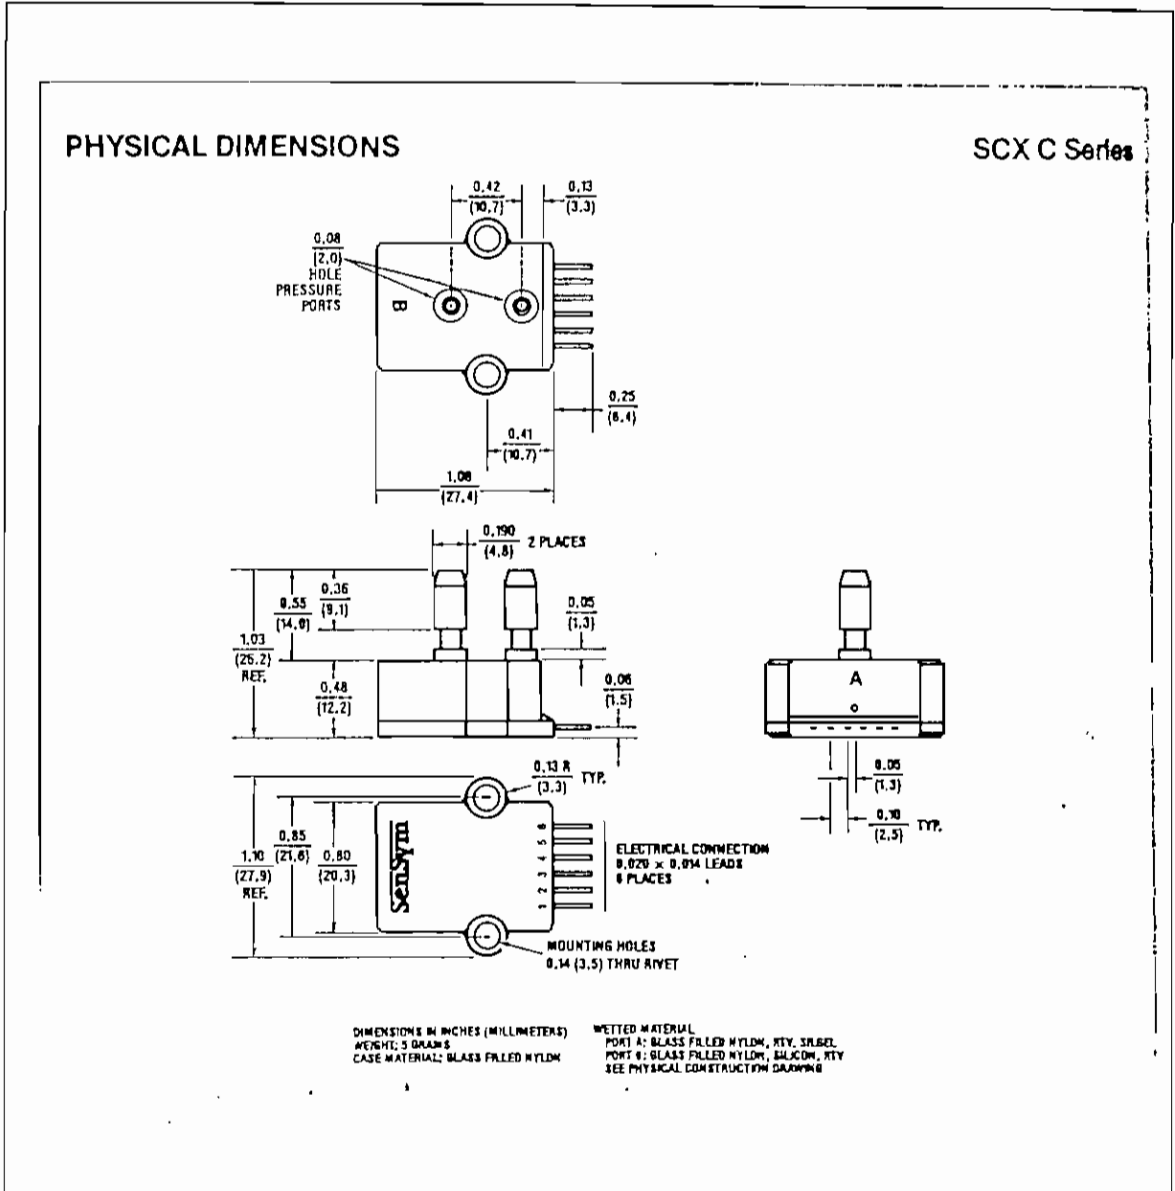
DIMENSIONES FISICAS DEL SENSOR SCX01DNC
